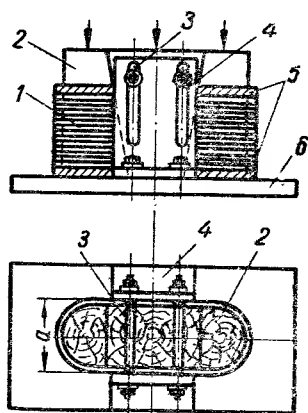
Приспособление для опрессовки катушек роторов с явно выраженными полюсами:
